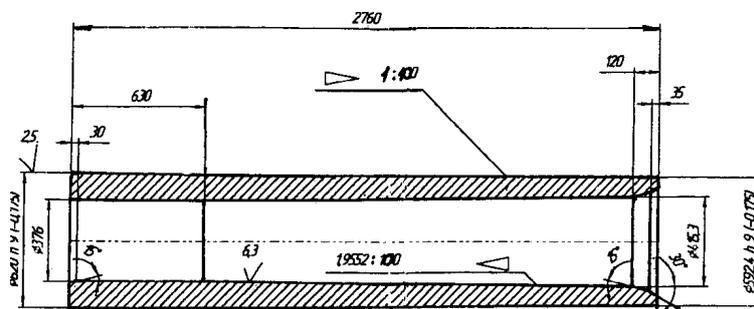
Калибровка вставки матрицы с измененной цилиндрической частью диаметром 376 мм и длиной 630 мм
